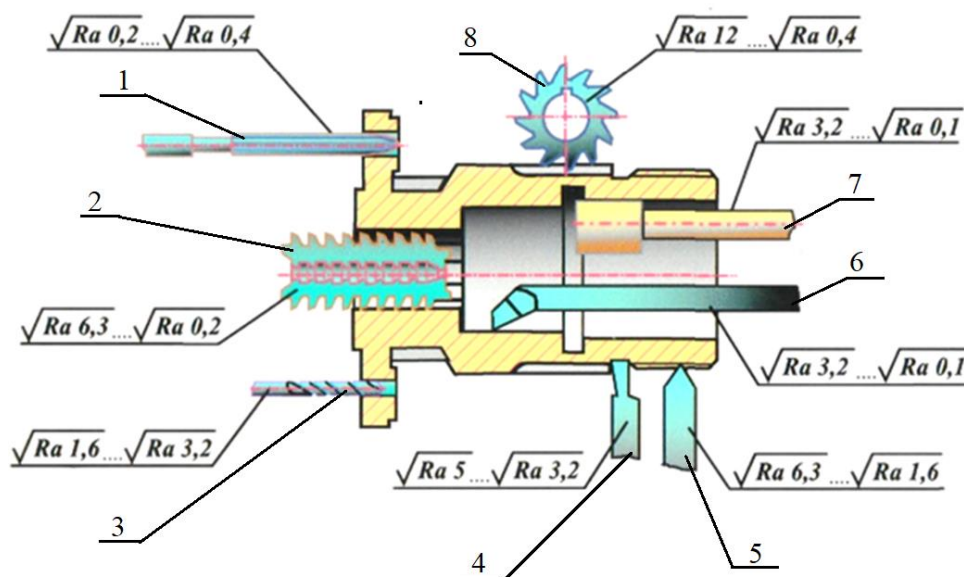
Шорсткість поверхонь, що оброблені різними інструментами.
